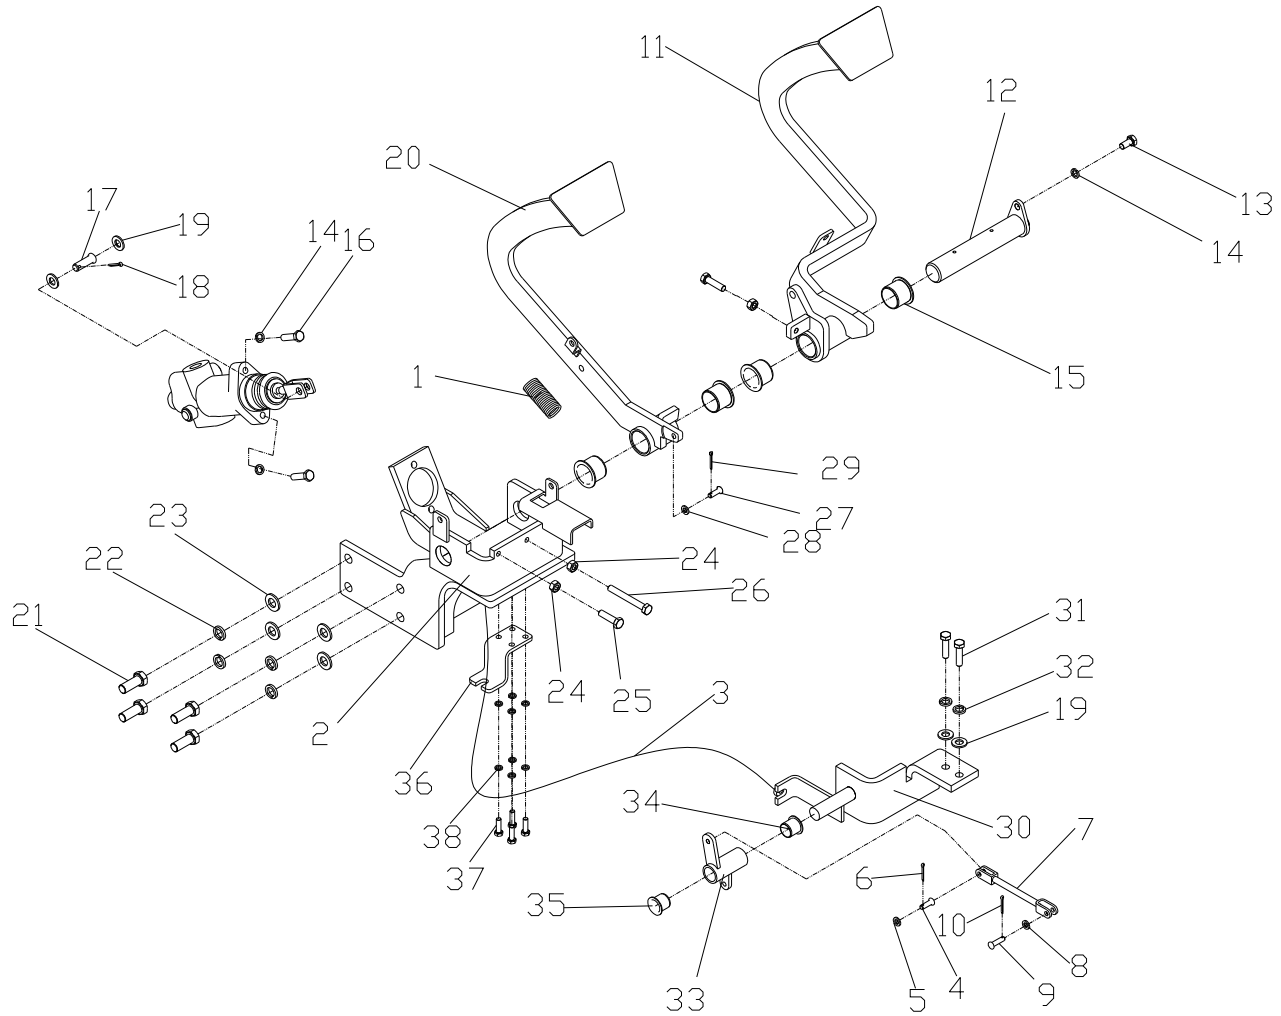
/Fig.1 制动微动操纵总成/Brake and inching assembly
